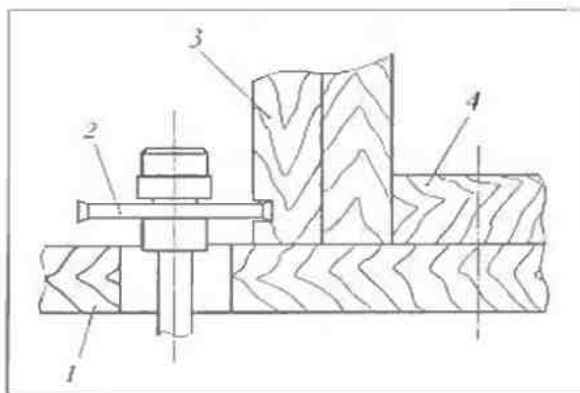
Фрезерование пазов в боковинах ящиков: 1 – рабочий стол; 2 – дисковая фреза; 3 – стенки ящиков; 4 – направляющая планка
